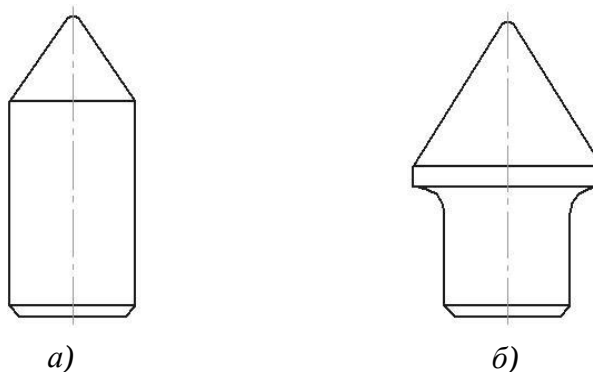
Твердосплавная вставка цилиндрической (а) и грибовидной (б) (ступенчатой) формы
